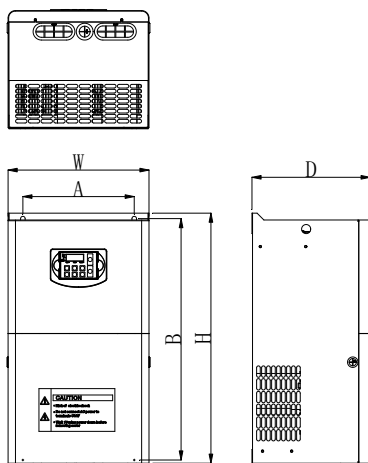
22~160KW 变频器外形尺寸及安装尺寸示意图
